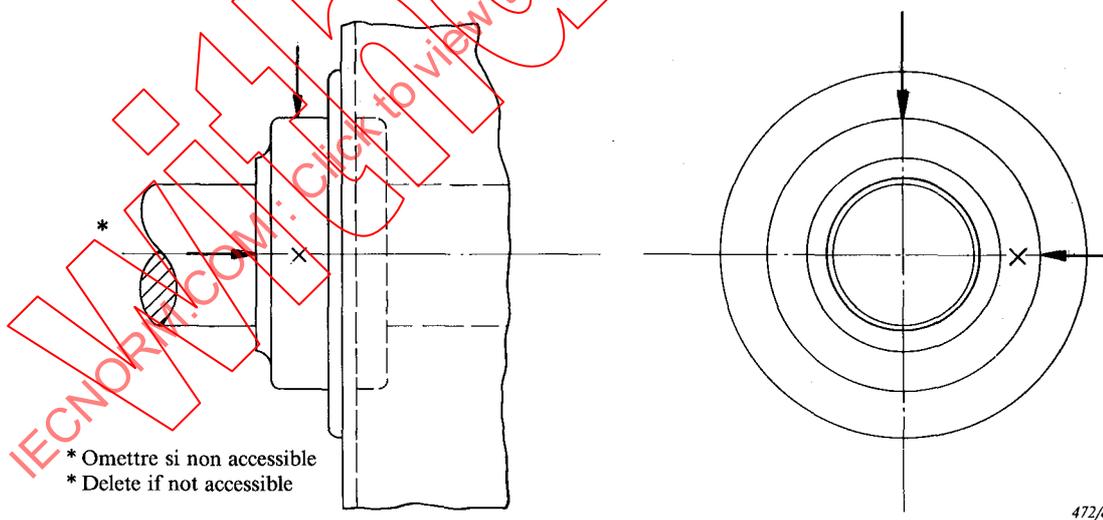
Emplacement des points de mesure pour des machines de hauteur d'axe supérieure à 400 mm, applicable aux deux extrémités de la machine.
